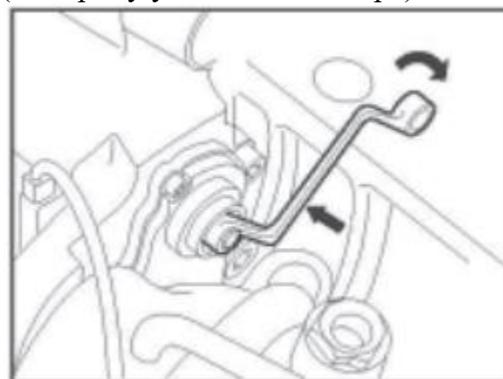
Проверка работы механизма автоматической регулировки зазора
